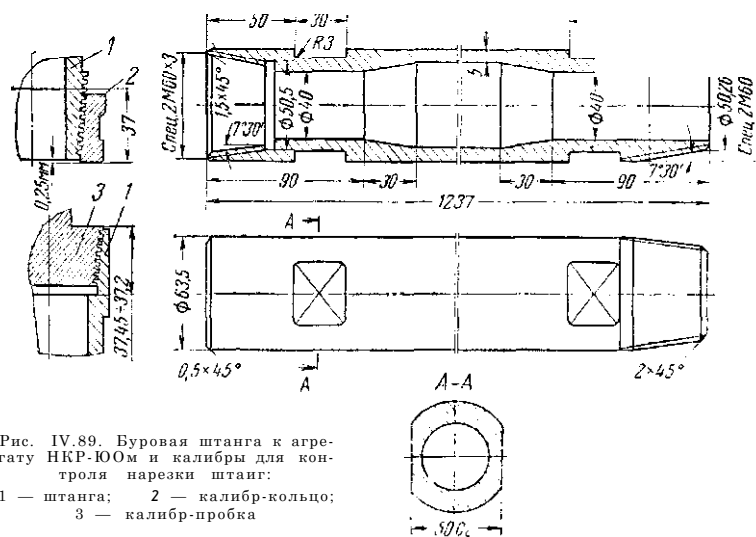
Буровая штанга к агрегату НКР-ЮОм и калибры для контроля нарезки штанг:
